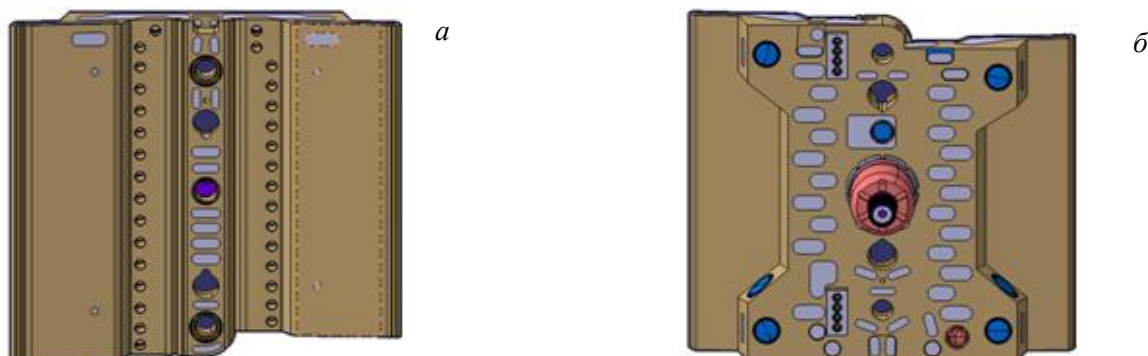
Общий вид НКПС для ППС 9 типа А: *а* — вид со стороны плазмы; *б* — вид со стороны ЗБ
